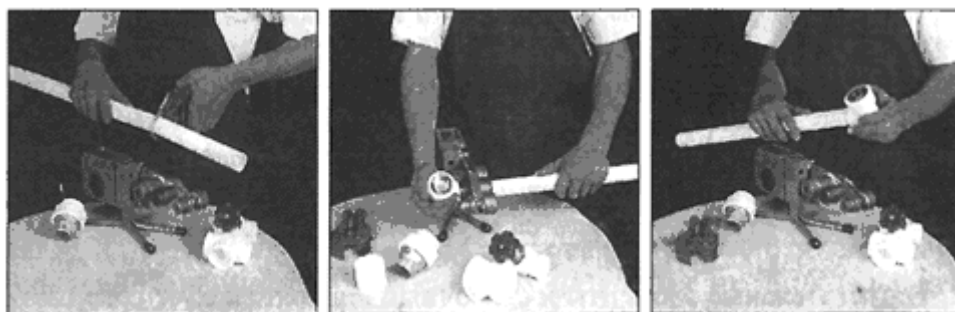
Основные операции раструбной сварки: резка, нагрев, соединение
